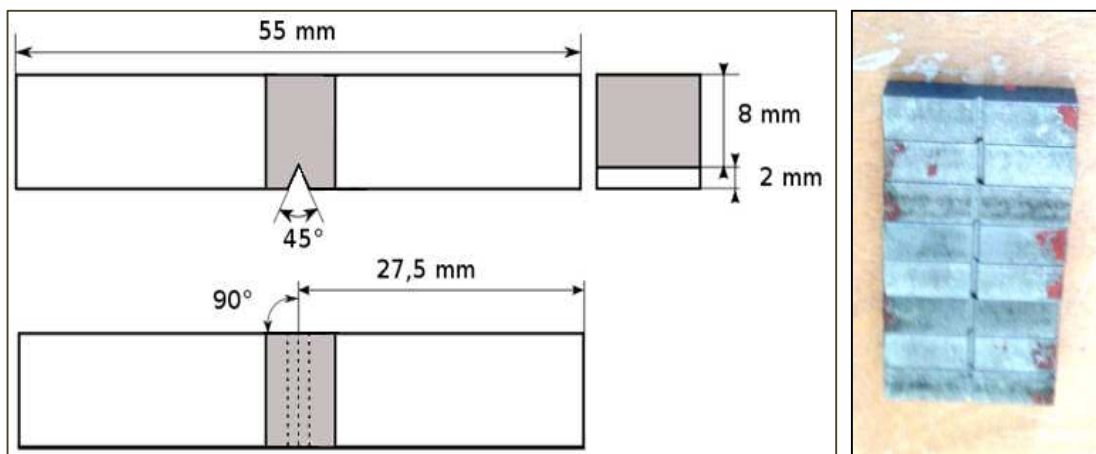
Dimensions et forme de l'éprouvette de l'entaille en V pour l'acier A510AP.
